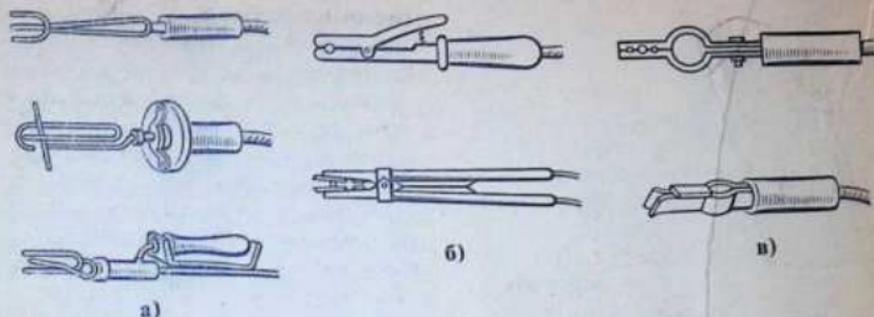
Электрододержатели для ручной дуговой сварки:
